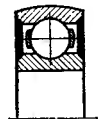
Шарикоподшипник со сферической поверхностью наружного кольца
